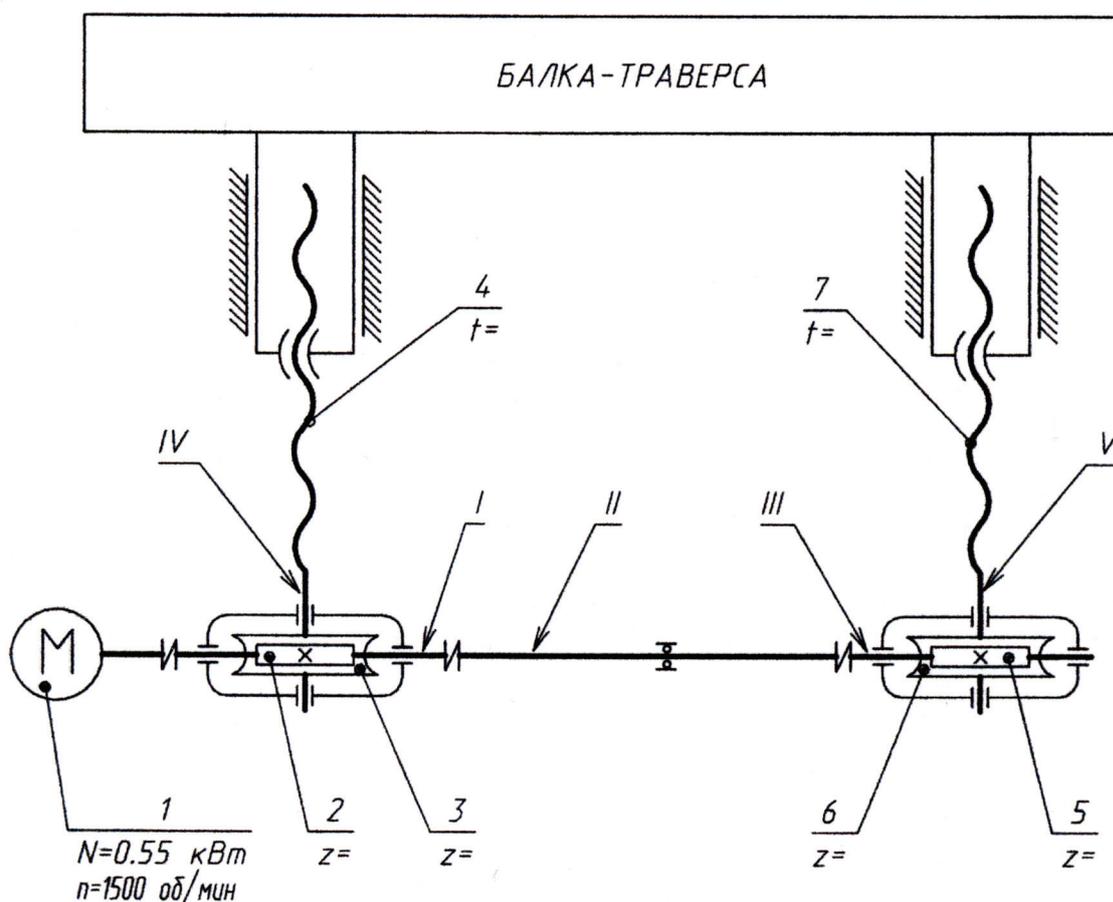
Кинематическая схема механизма подъема балки-траверсы
